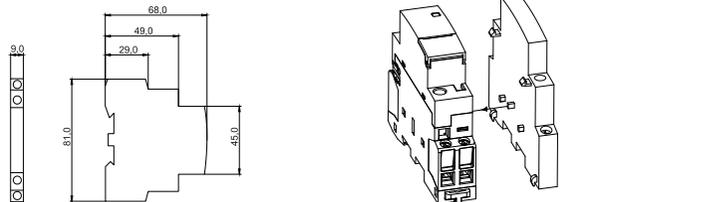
Габаритные размеры контакта дополнительного / Figure 2 – Overall dimensions of auxiliary contact
